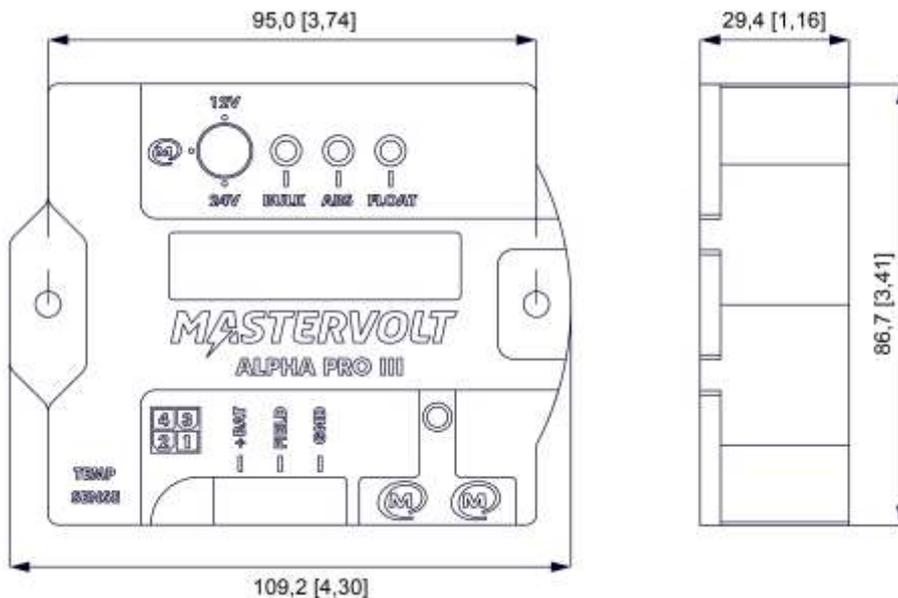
Schémas des dimensions du régulateur Alpha Pro en mm [pouces]
